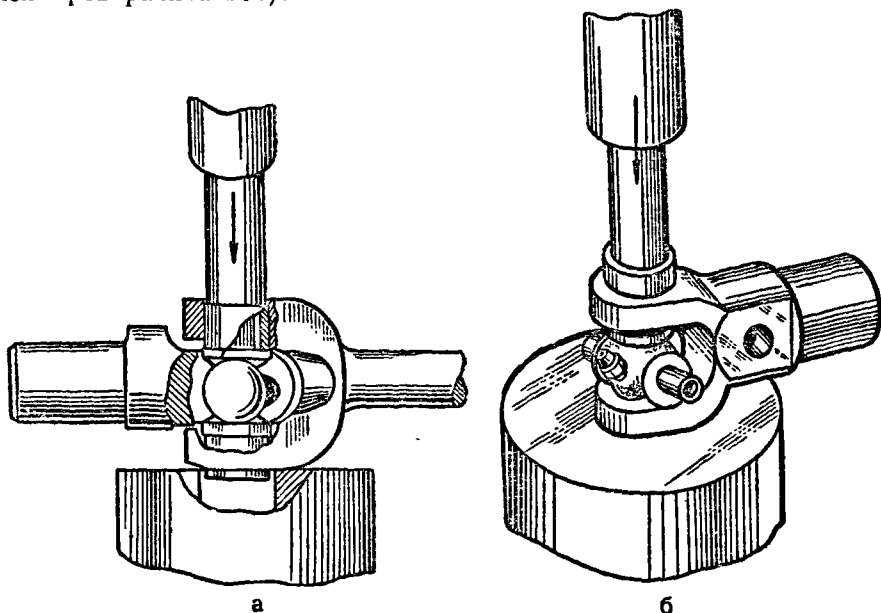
Выпрессовка (а) и запрессовка (б) игольчатого подшипника крестовины карданного вала
